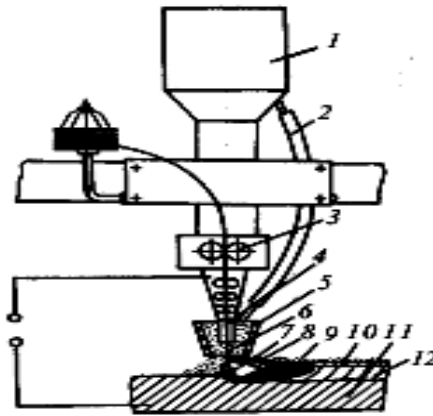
Схема автоматичної наплавки під флюсом.
